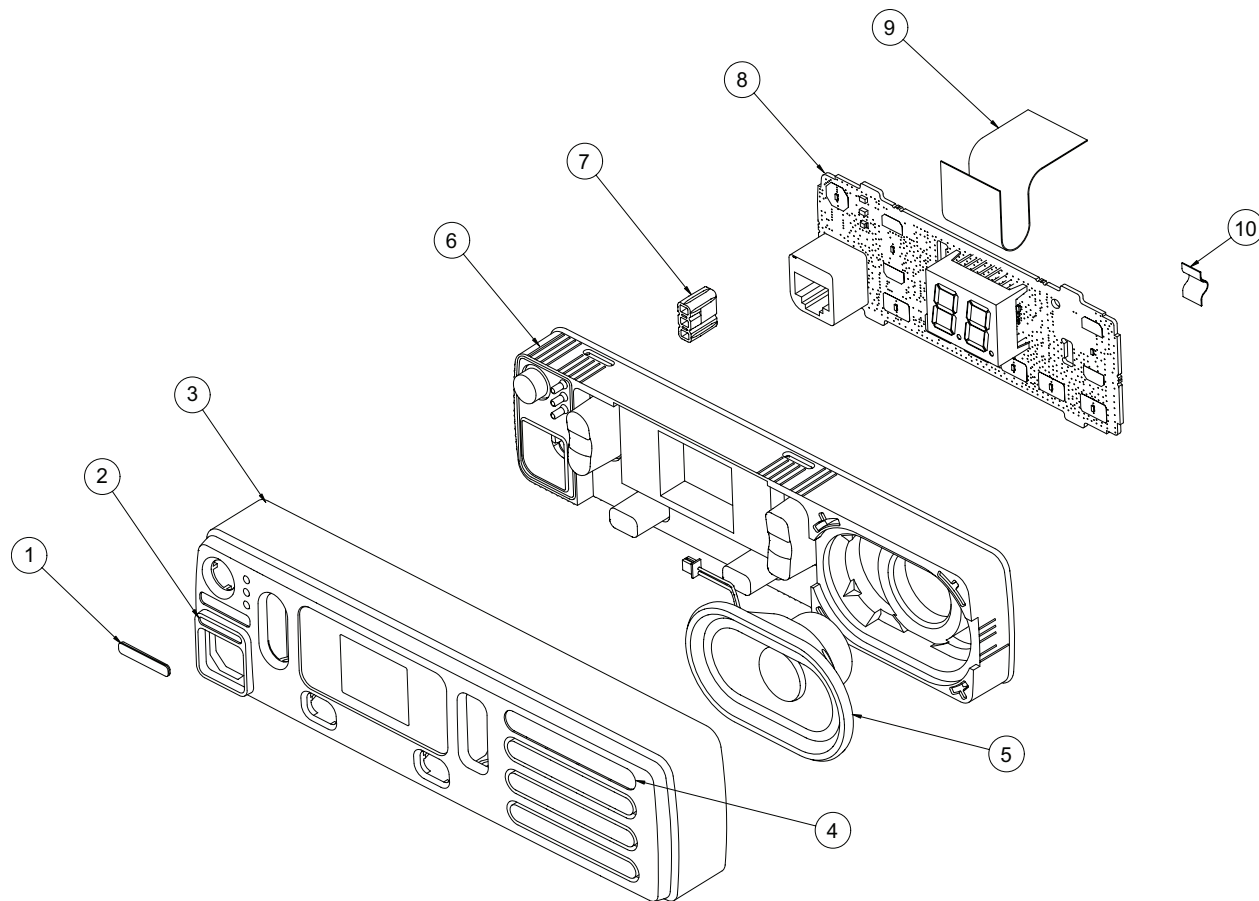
Vista del despiece del cabezal de la pantalla numérica
